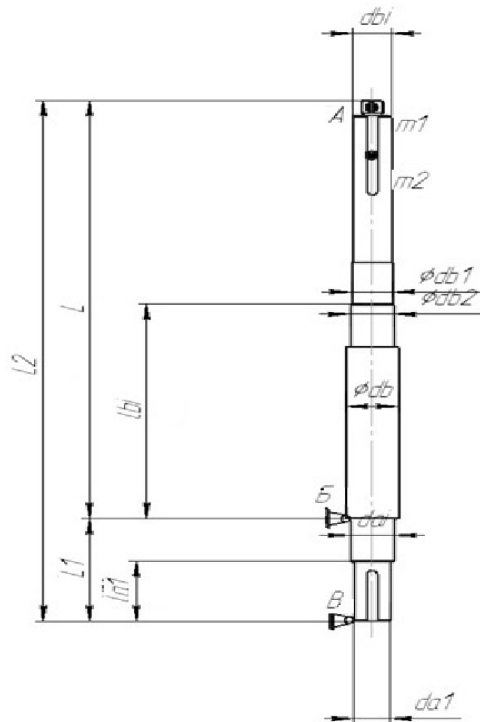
Розрахункова схема консольного ступінчатого вала
